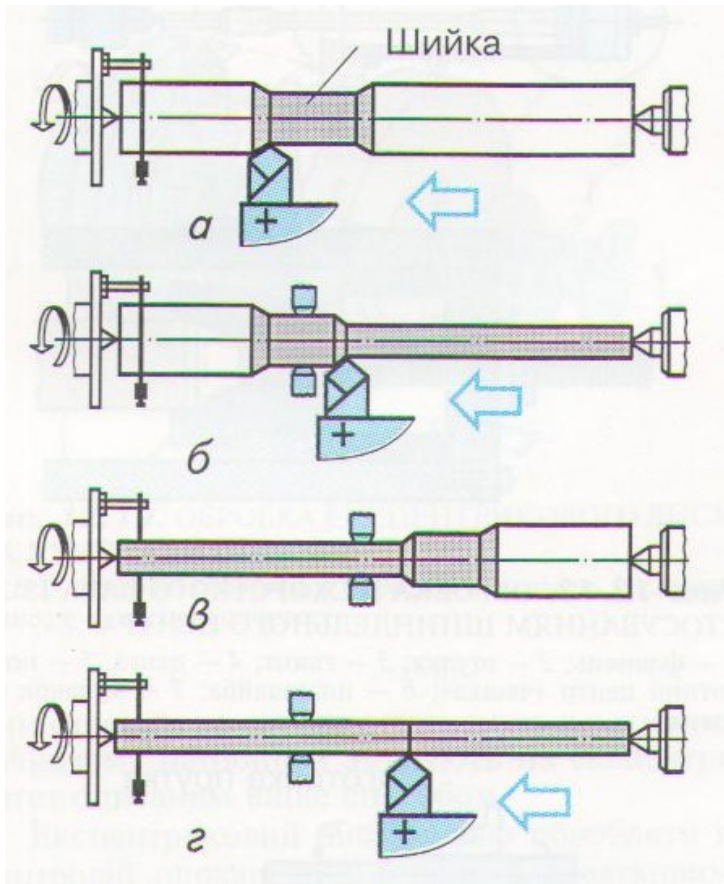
Технологічна схема обробки нежорсткого вала:
